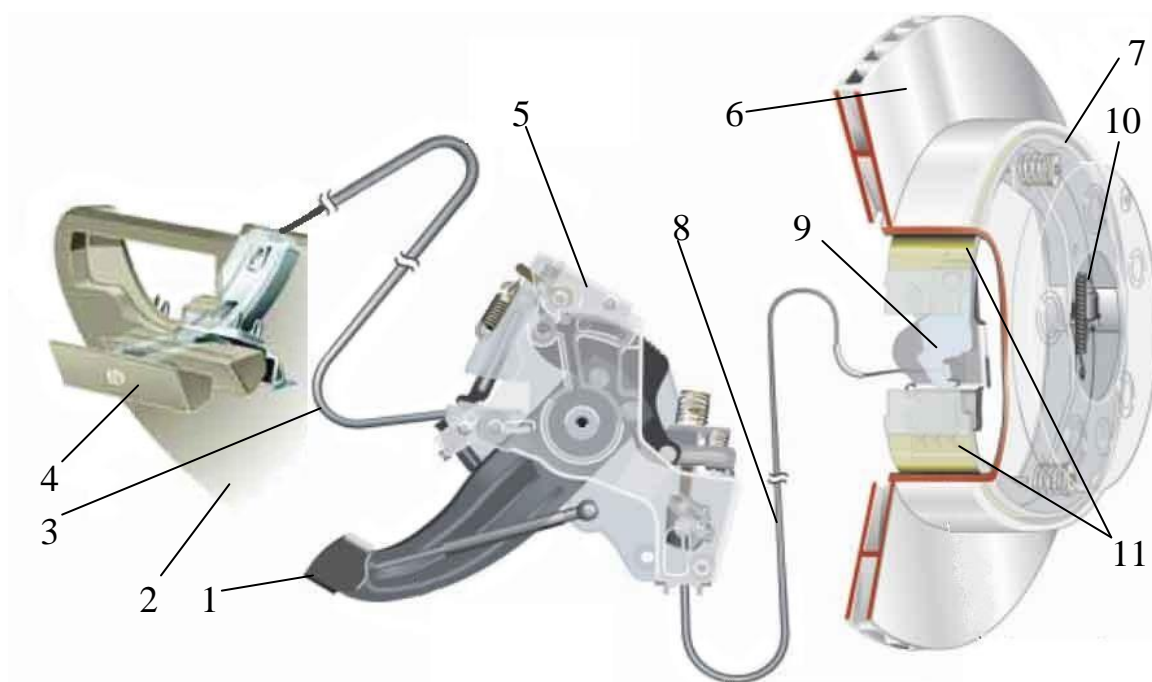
Механический привод стояночного тормоза легкового автомобиля Audi Q7: 1 – педаль управления стояночным тормозом; 2 – передняя панель салона автомобиля; 3 – трос привода механизма разблокировки; 4 – рукоятка разблокировки стояночного тормоза; 5 – узел педали привода стояночного тормоза; 6 – диск тормозного механизма рабочей тормозной системы; 7 – встроенный барабанный тормозной механизм стояночной тормозной системы; 8 – трос привода тормозных механизмов; 9 – разжимной механизм; 10 – регулировочный винт; 11 – тормозные колодки
